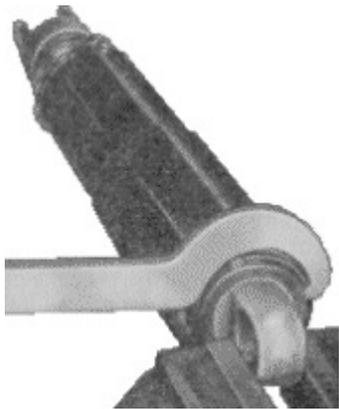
Abschrauben der Ringmutter mit dem Hakenschlüssel 05 MW 28-3
